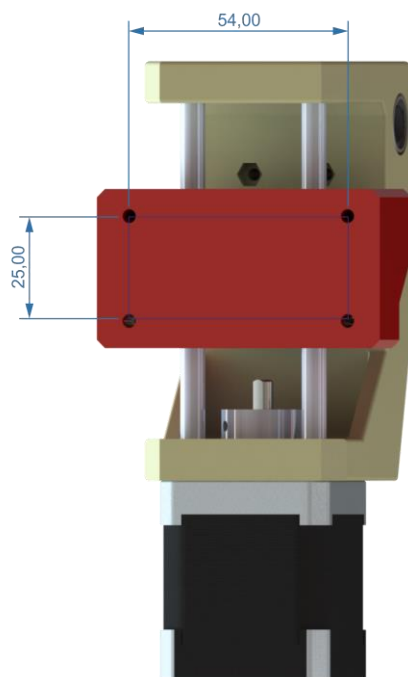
Присоединительные размеры крепления модулей рабочего инструмента
